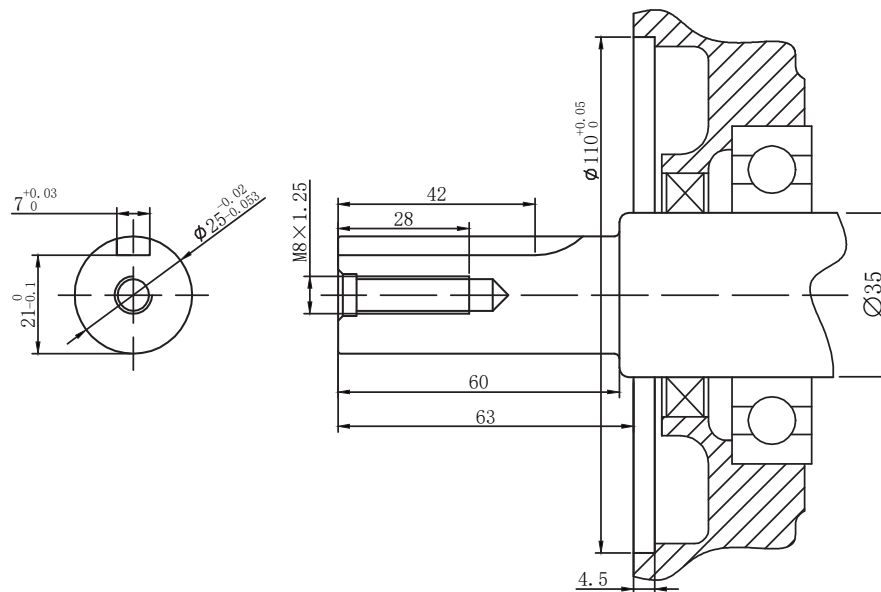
, Zeichnung der Welle des Motors Heron® 8896770
